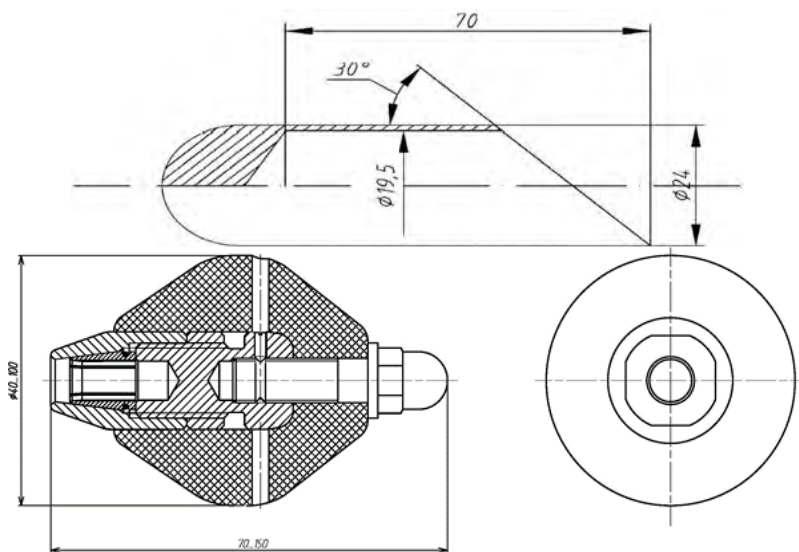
Примерный вид колпачка для проталкивания прядей каната
